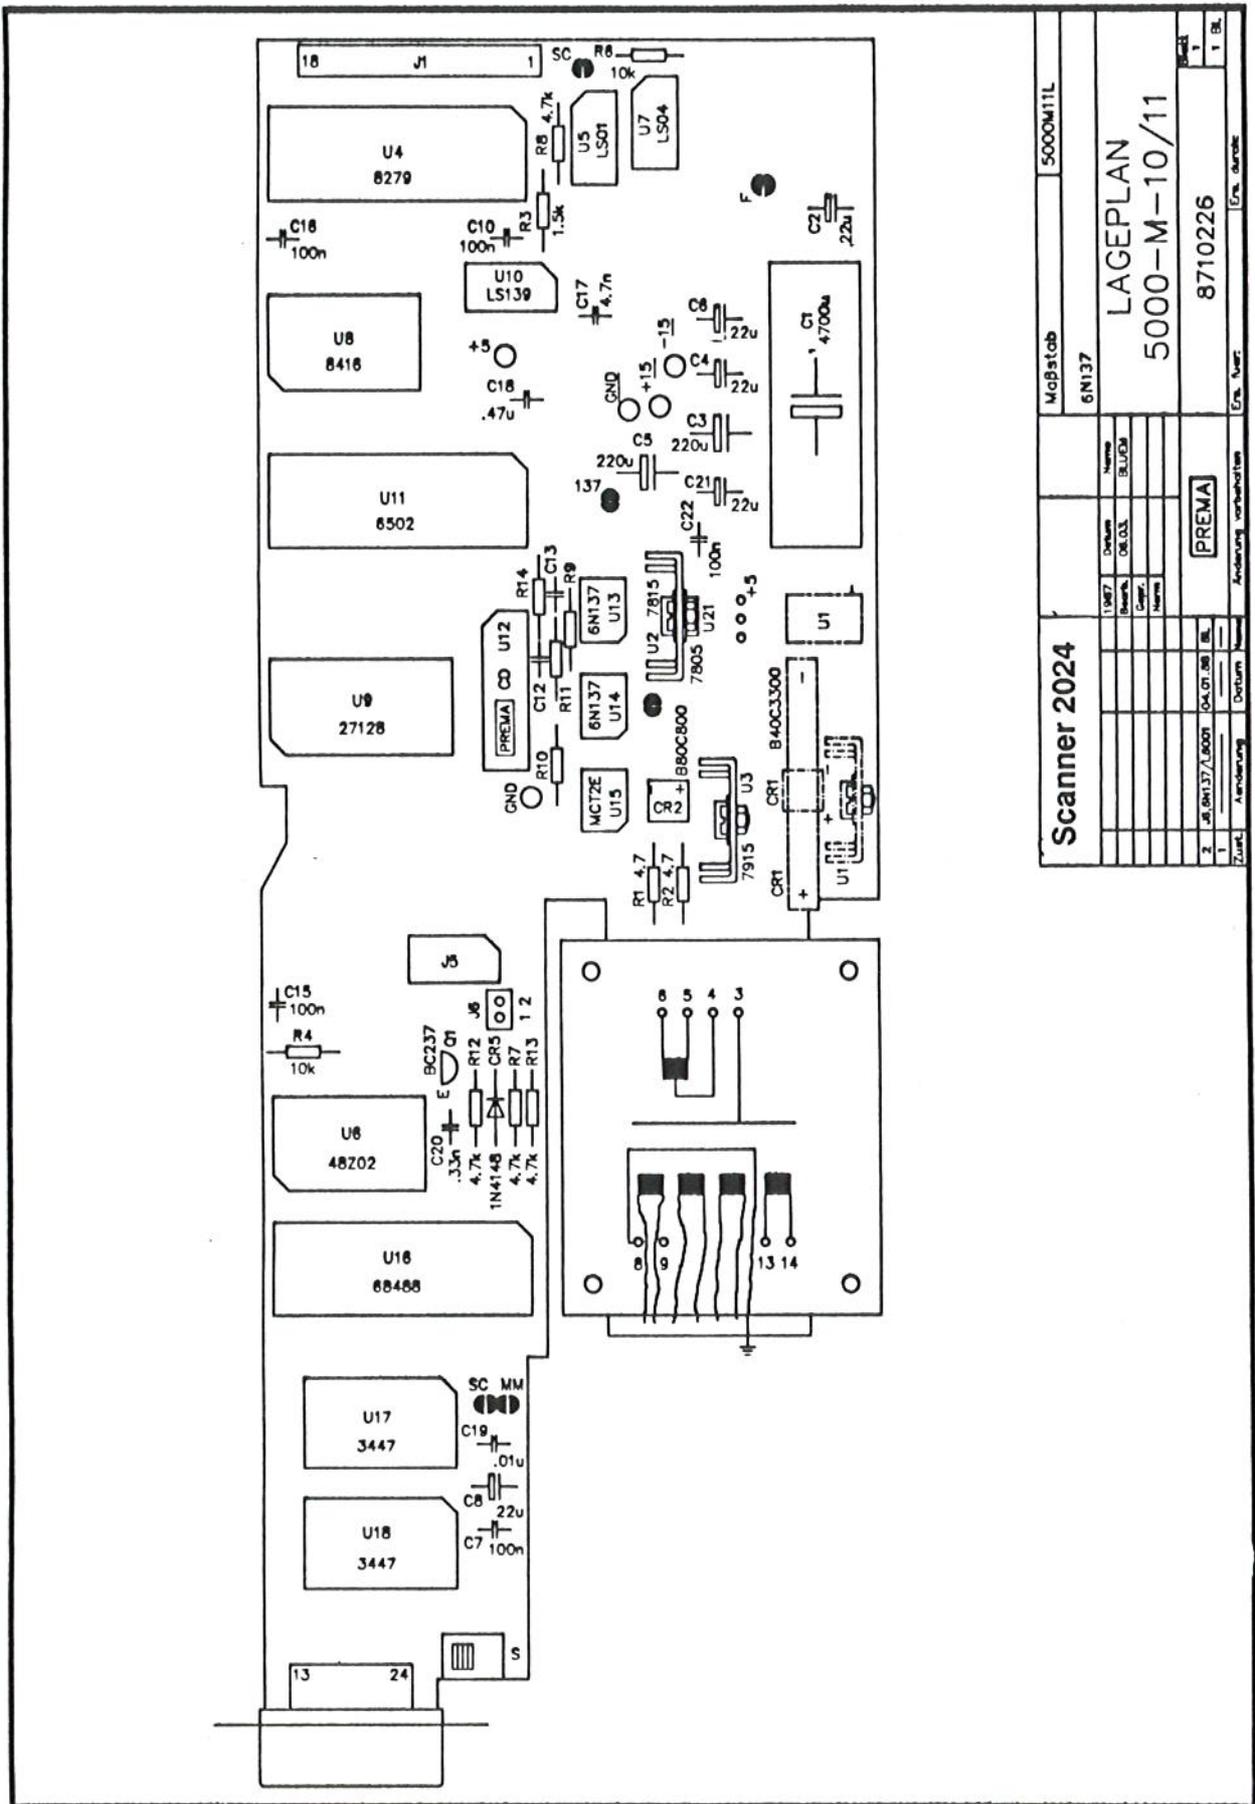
Lageplan der Mikroprozessorplatte Scanner 2024
